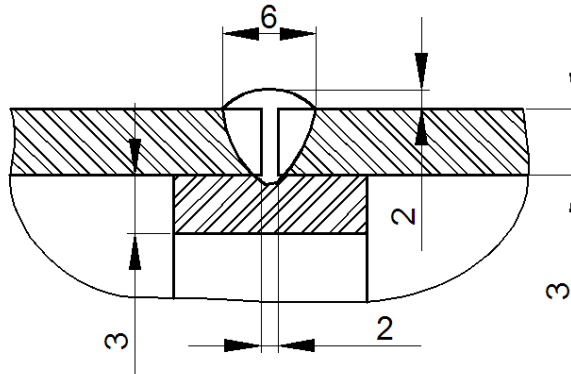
Схема зварного стикового з'єднання С5 за ГОСТ 8713-79
